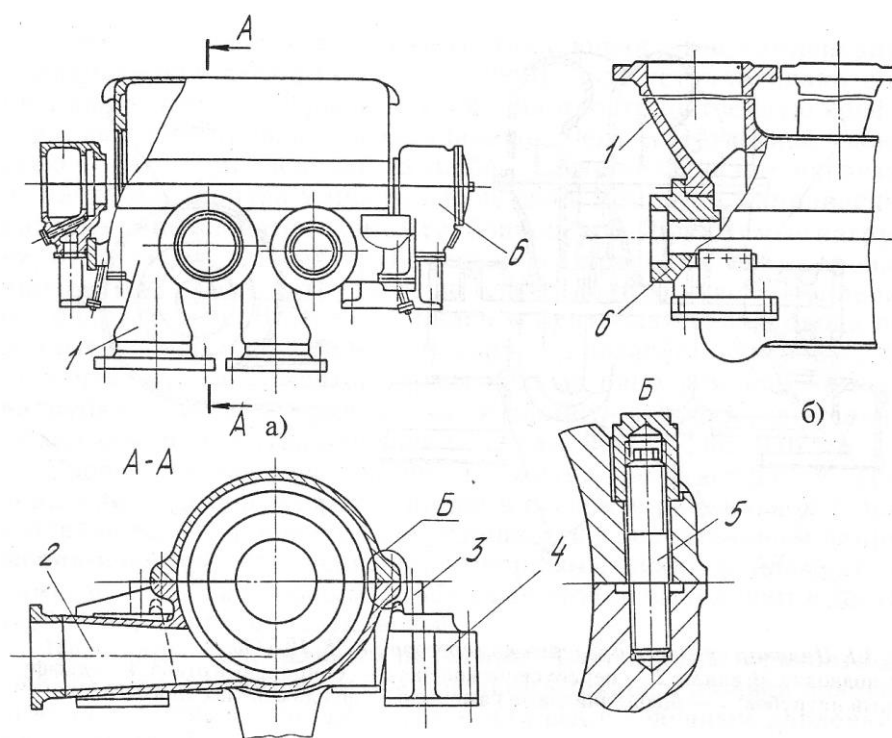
Корпуса унифицированных центробежных компрессоров НИИТК - ККЗ: а – б – соответственно с нижним и верхним расположениями патрубков; 1 – всасывающий патрубок; 2 – нагнетательный патрубок; 3 – установочные лапы; 4 – фундаментальная рама; 5 – стяжные шпильки; 6 – корпуса подшипников.
